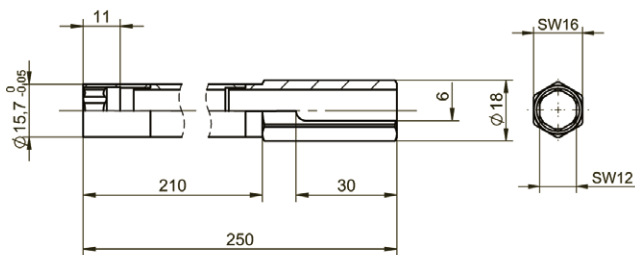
Montageschlüssel Ø18/SW16 Typ 1300B7 für Einbaubohrung > Ø16 mm
